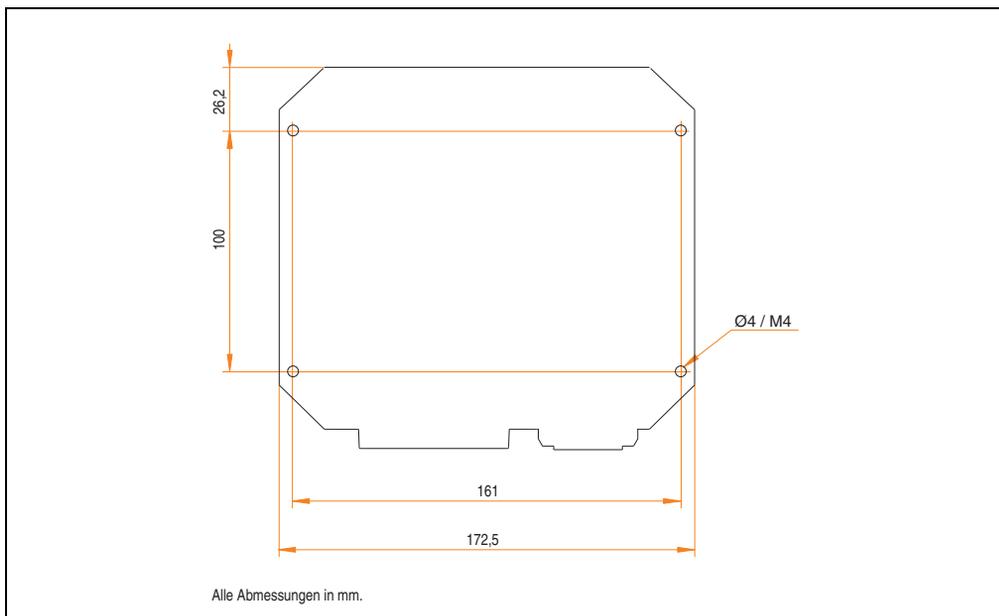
Bohrschablone 4MPCBX.0000-00
